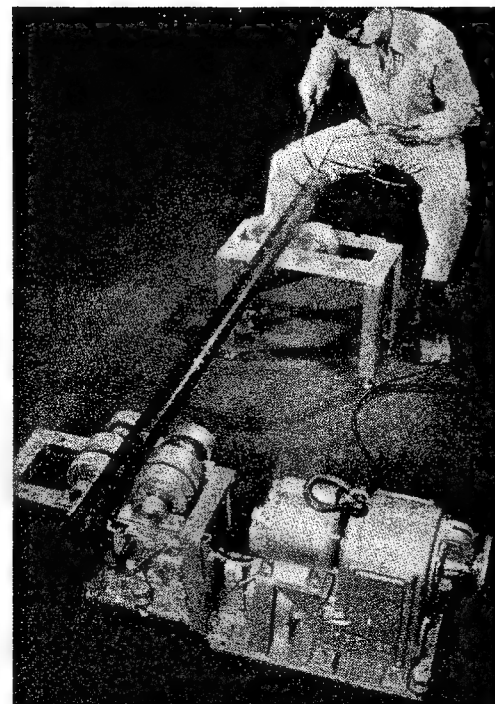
Aparato rotatorio para facilitar la soldadura de tubos, accionado por pedal.
